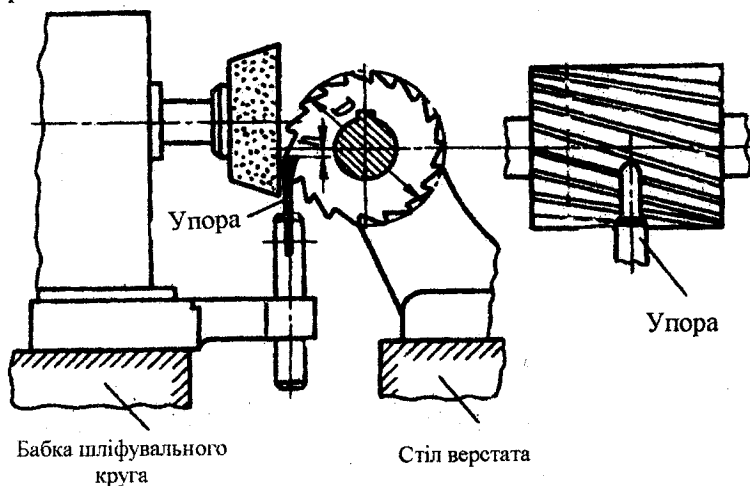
Схема заточування циліндричної фрези з гвинтовими канавками
